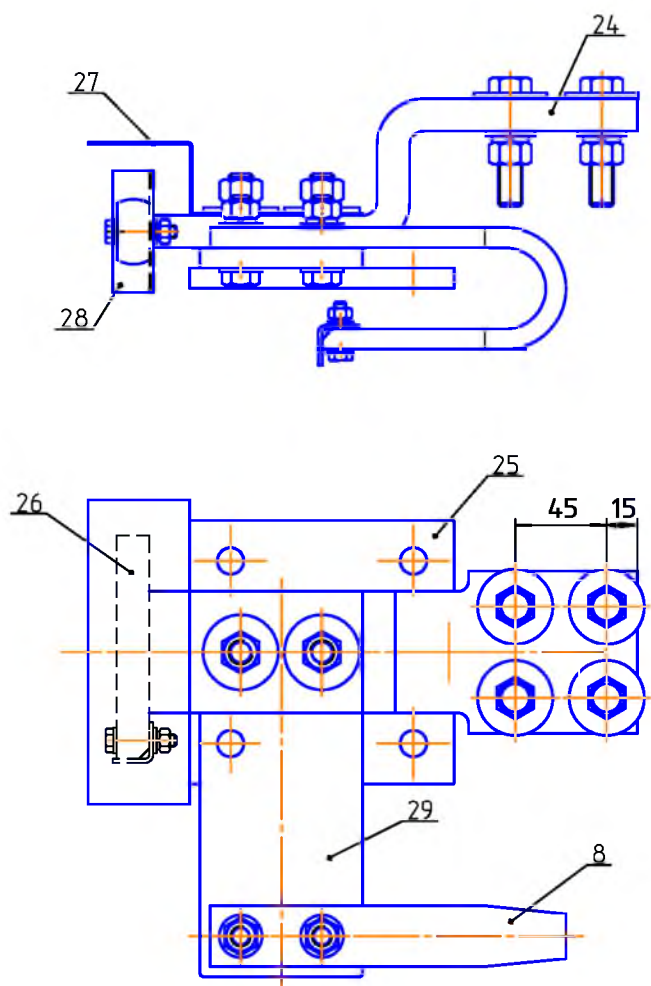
Неподвижный нож контактный разъединителя РГП СЭЦ®-35/2000
